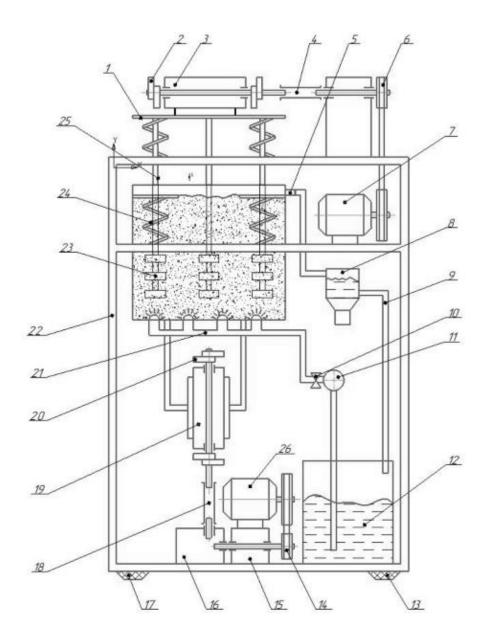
Вибростанок с резервуаром цилиндрической формы поперечного сечения
